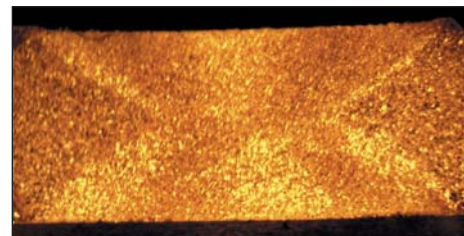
Макрошлиф поперечного сечения образца двухстороннего сварного шва из сплава М1
